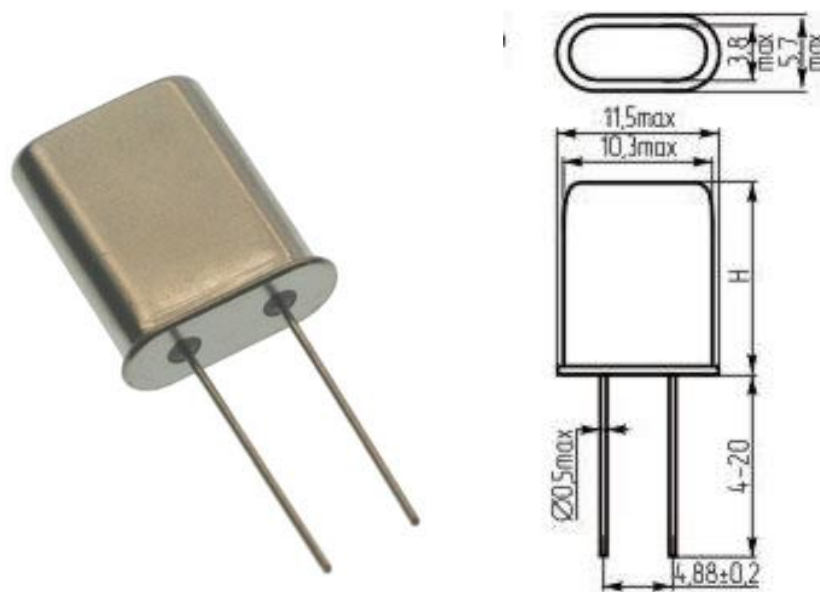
Габаритні розміри резонатора КХ-3НТ
